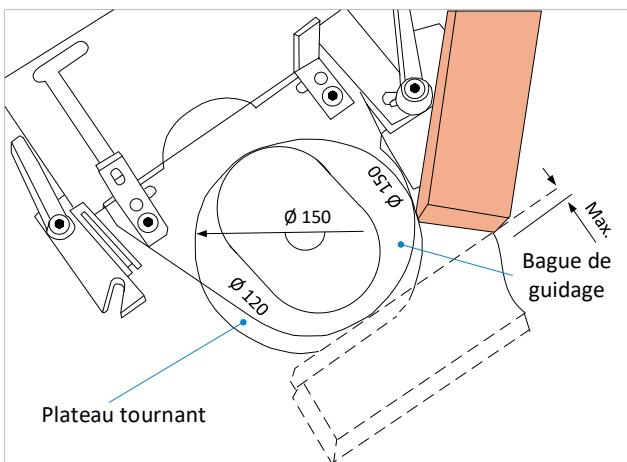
Réglage du guide de fraisage courbe TAPOA 1639
